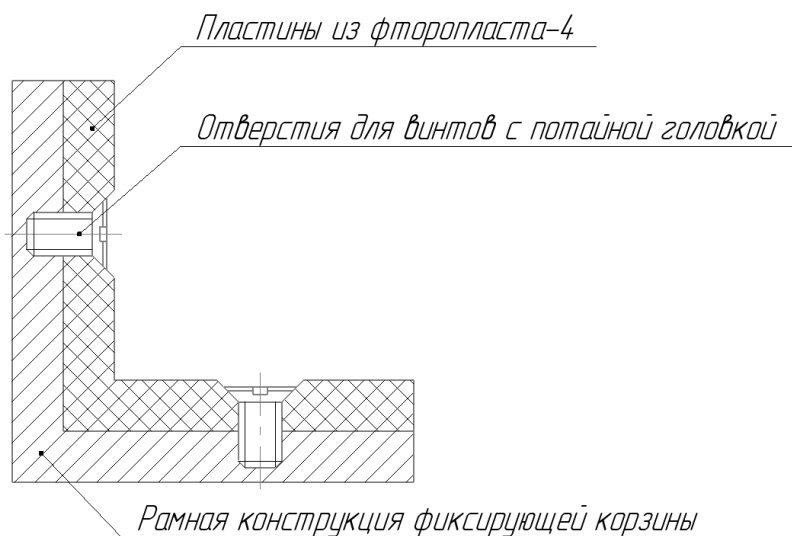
Схематичное представление способа фиксации фторопластовых накладок
